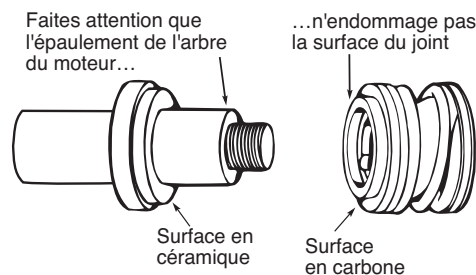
PROTÉGER LES SURFACES DU JOINT
